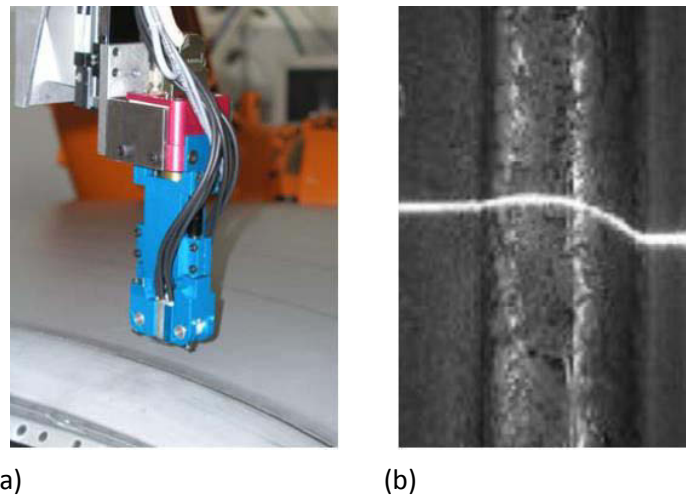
Inspection de joint de soudure: (a) la tête de capteur, comprenant la caméra CMOS (en rouge), le laser et une source lumineuse (en bleu), contrôle un joint de soudure laser à l'aide d'une raie laser, (b) image du joint soudé par laser et de la ligne laser projetée (Source : Photonfocus) .
